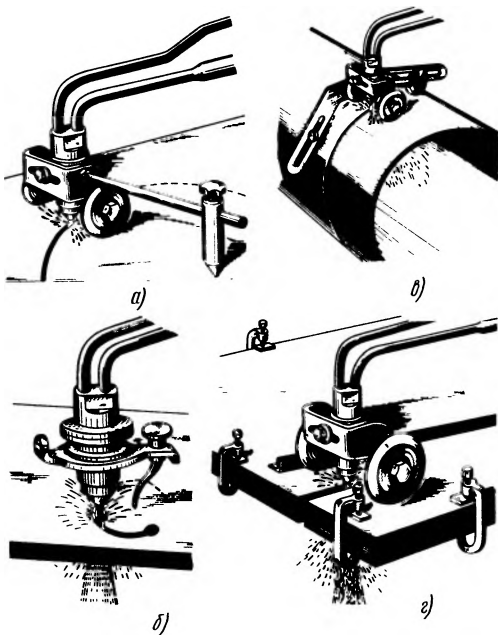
Приспособления к резаку: а – для вырезки фланцев, б – для вырезки отверстий, в – для резки труб, г – для пакетной резки
